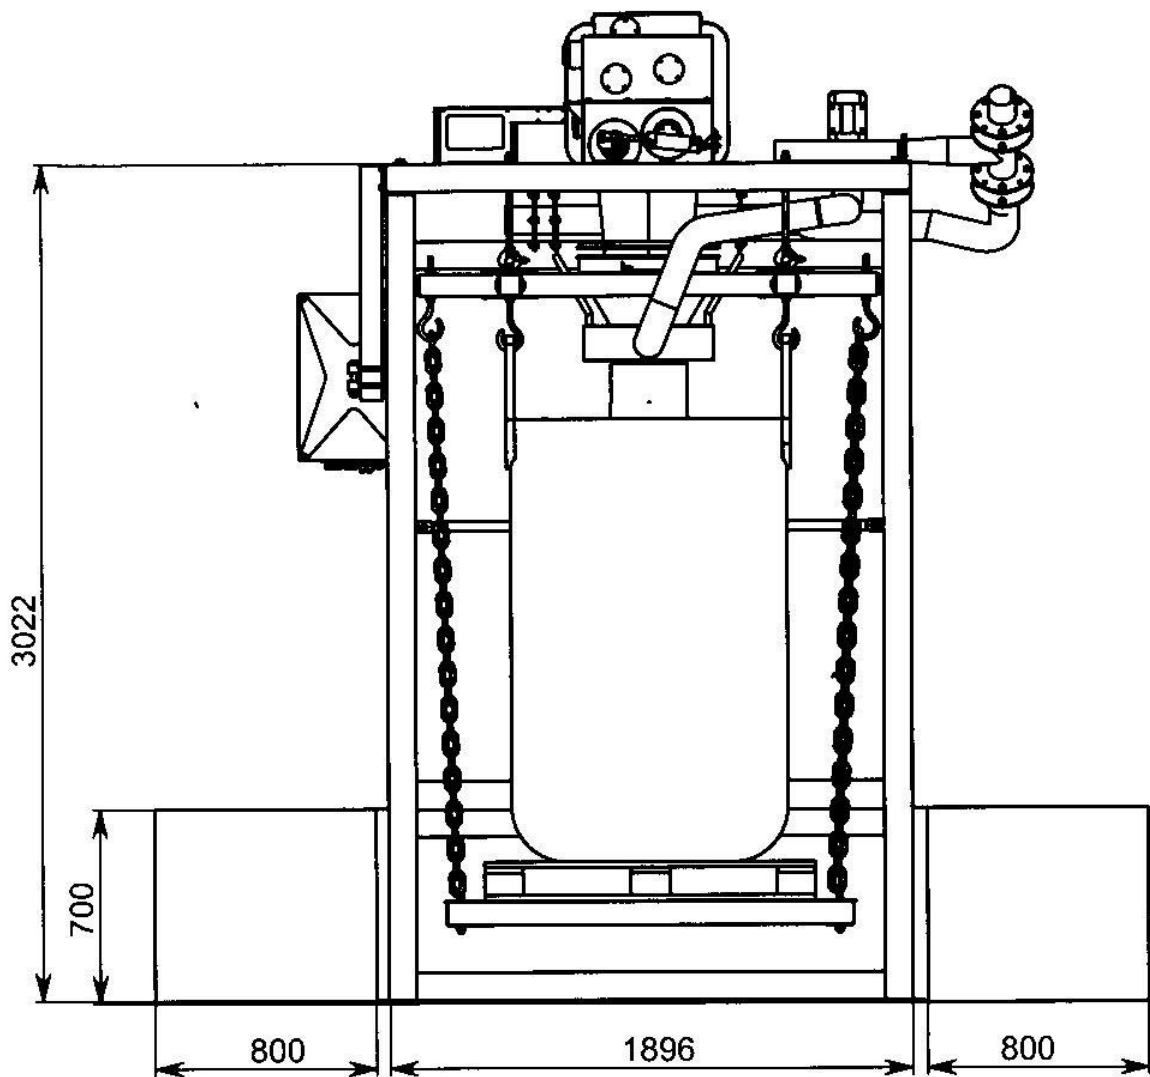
Габаритно-установочные размеры дозатора. Вид спереди.
